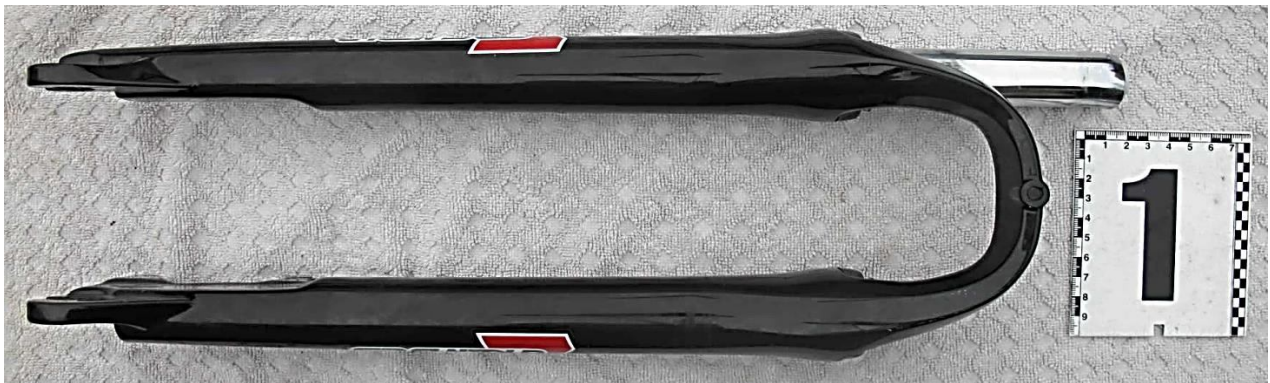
Загальний вигляд спереду передньої вилки велосипеда із зруйнованими амортизаторами
